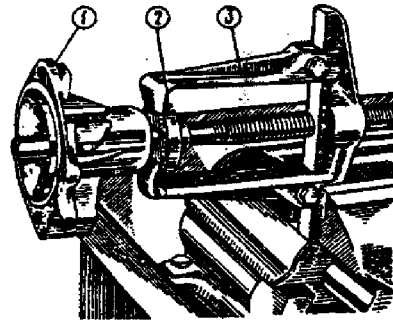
Desmontagem do cubo da polia: 1 - tampa do corpo da bomba; 2 - cubo da polia; 3 - extrator.
